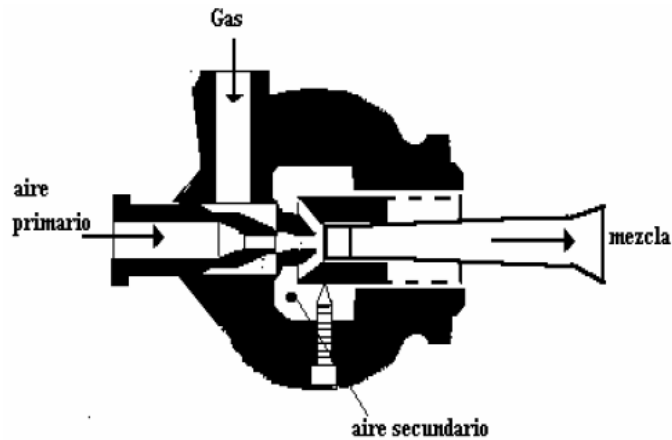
Quemador de aire inductor con gas a la presión de la línea. [8]
